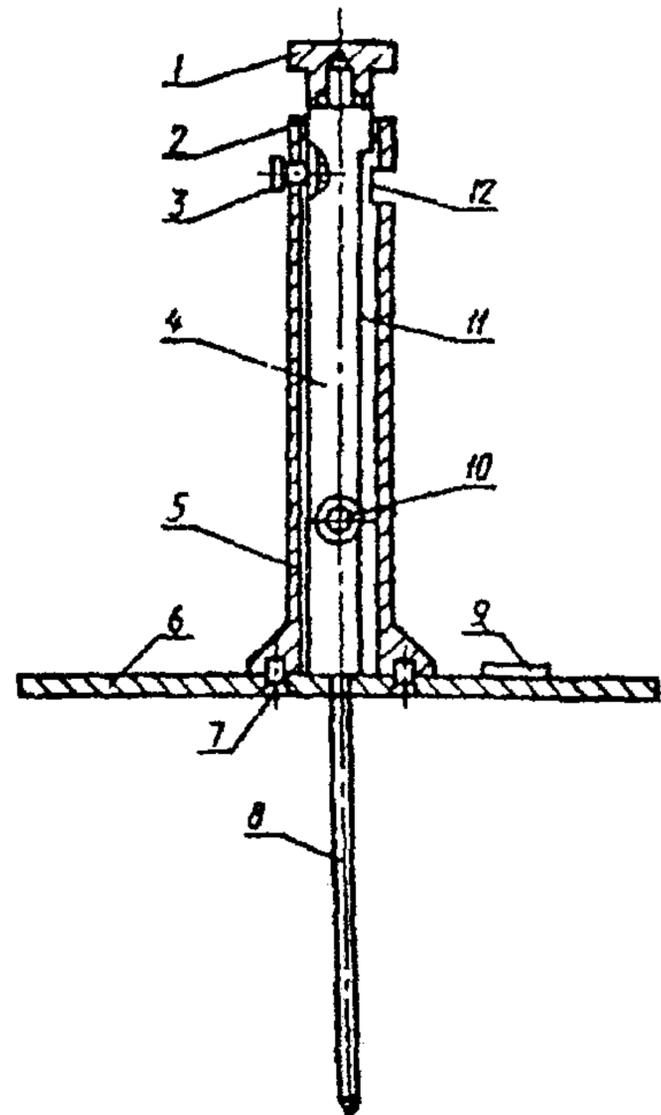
1 — ручка, 2 — втулка, 3 — зажимной винт, 4 — вставка, 5 — корпус, 6 — основание, 7 — крепежный винт, 8 — игла, 9 — табличка, 10 — крепежный винт, 11 — шкала, 12 — стекло
